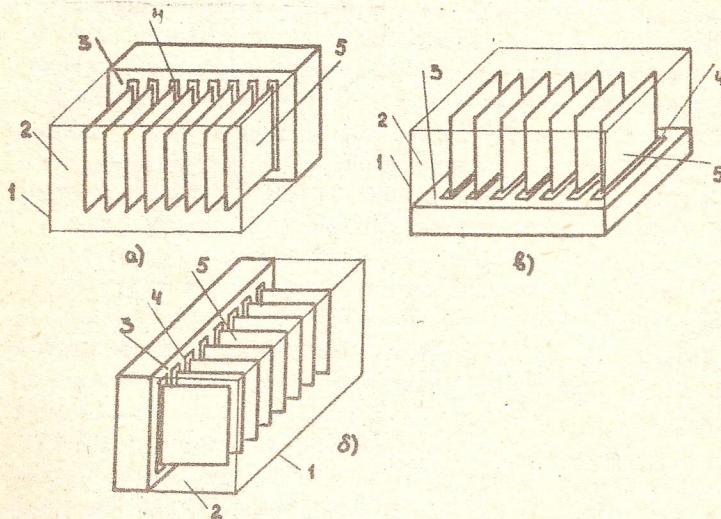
Вертикальное поперечное (а), вертикальное продольное (б) и горизонтальное (в) расположение монтажной панели в блоках разъемной конструкции:
